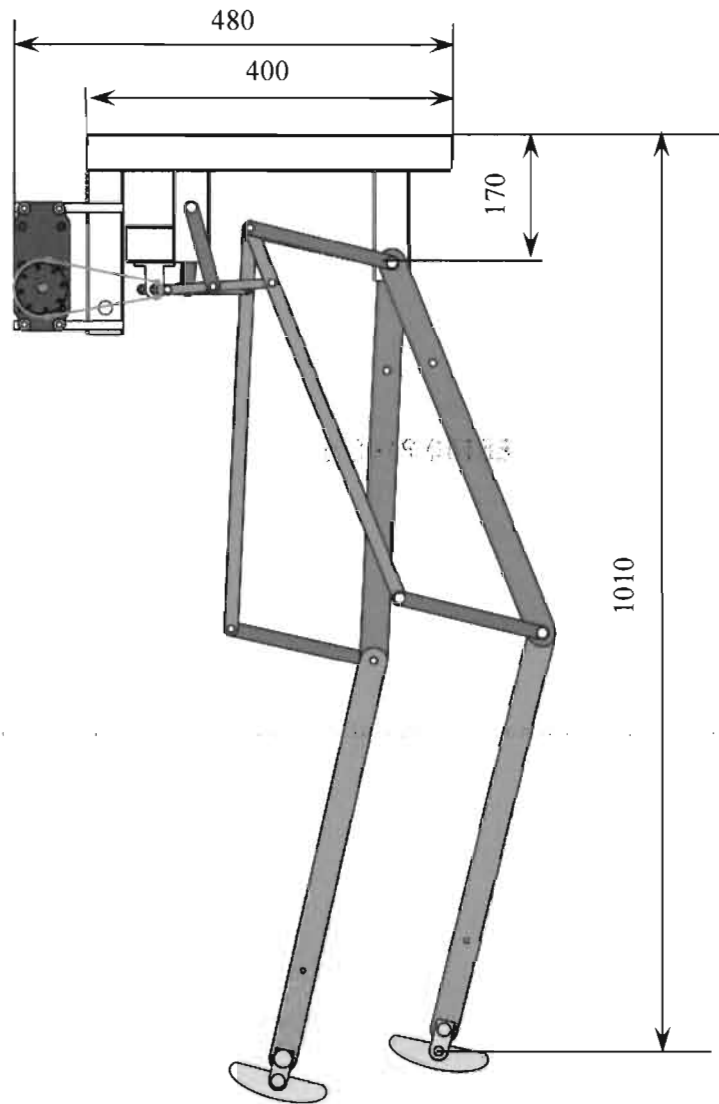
Dimensiuni de gabarit ale ansamblului exoschelet, în [mm].
